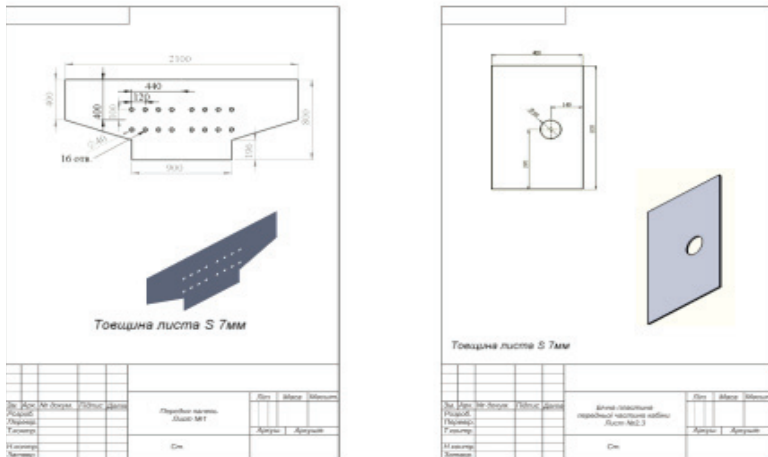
Зразки елементів креслення пластин для бронювання автомобіля КраЗ
